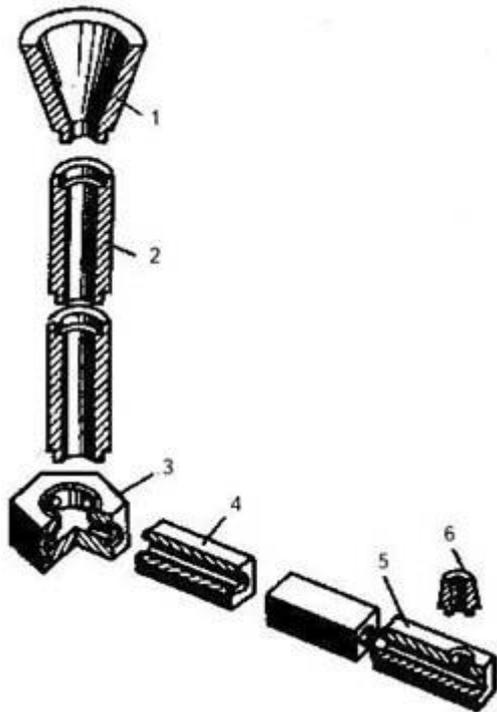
Разновидности сифонного кирпича: 1 - воронка; 2 - шаматная трубка; 3 - звездочка; 4 - трубка сифонная пролетная; 5 - трубка сифонная концевая; 6 - стаканчик для изложницы
